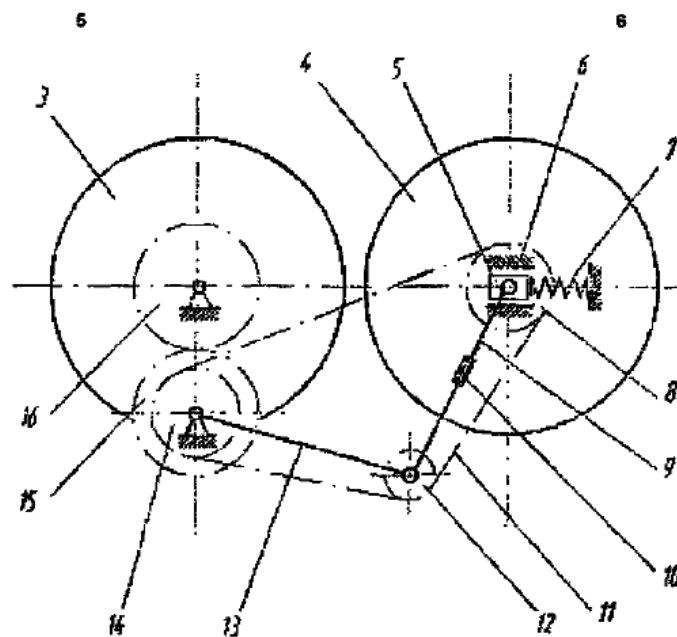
Кінематична схема передаточного механізму валкової дробарки
